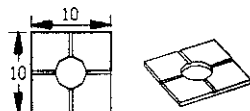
Widia de corte que gerou o defeito no rolamento
